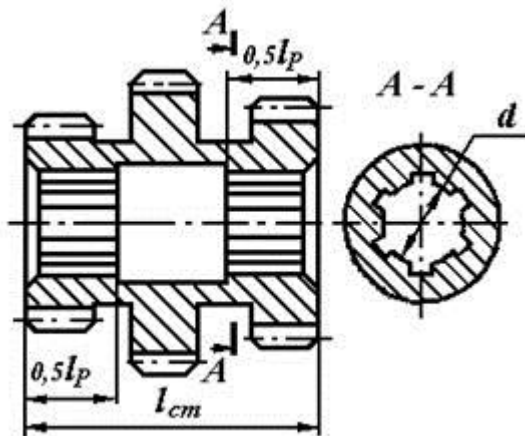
Шлицевое соединение блока шестерен с валом коробки передач
